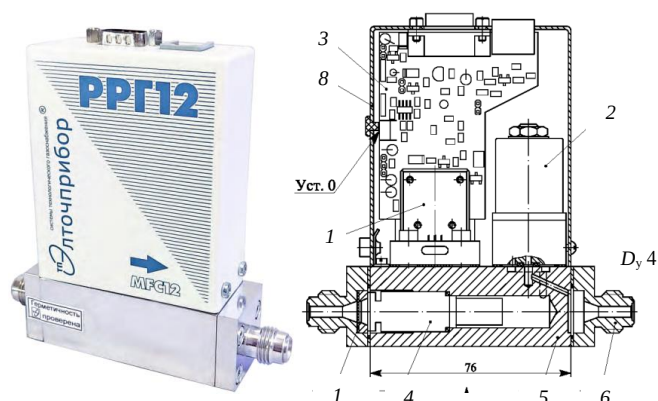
Регулятор расхода газа РРГ-12: 1 – преобразователь первичный, 2 – механизм исполнительный, 3 – усилитель измерительный, 4 – байпас, 5 – корпус, 6 – штуцер, 7 – сетка-рассекатель, 8 – крышка
